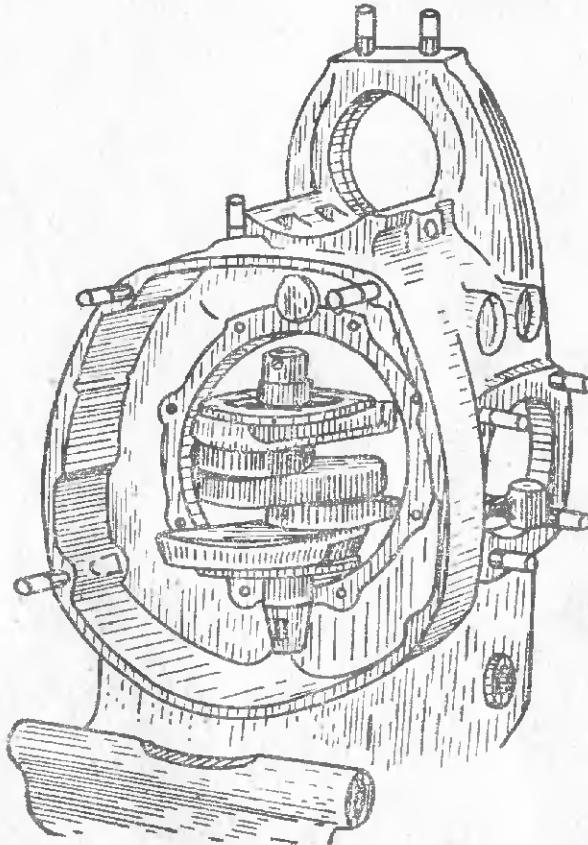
Ориентировка коленчатого вала при его монтаже и демонтаже
